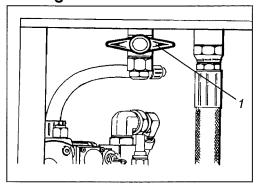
Réservoir hydraulique, dessous 1 robinet de vidange
